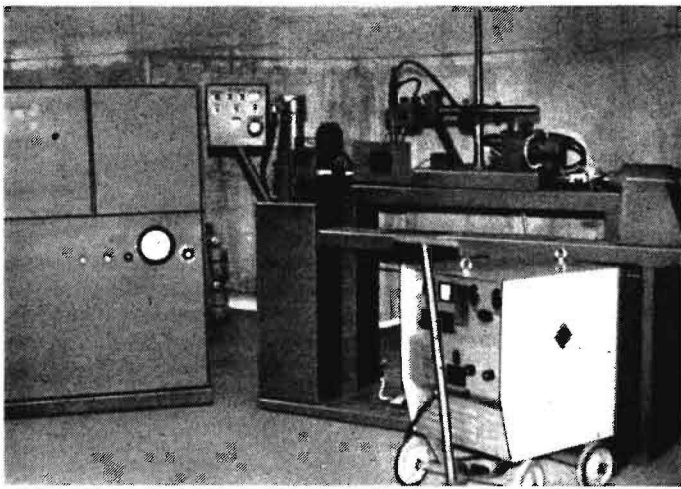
MAG-Schweißanlage SM-05/R. bestehend aus Grundschweißgerät, Steuerschrank und Stromversorgungsgerät
